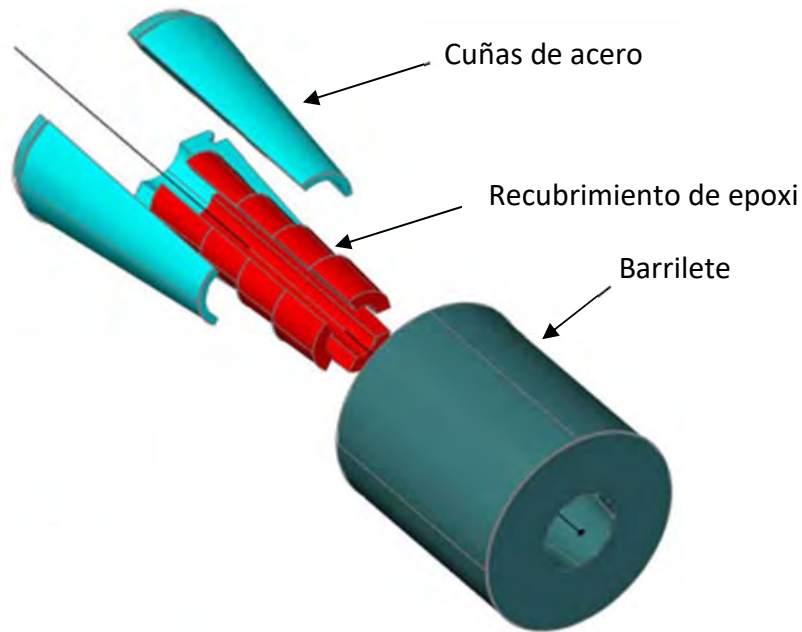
Conjunto de Anclaje: Barrilete, cuñas de acero, epoxi
